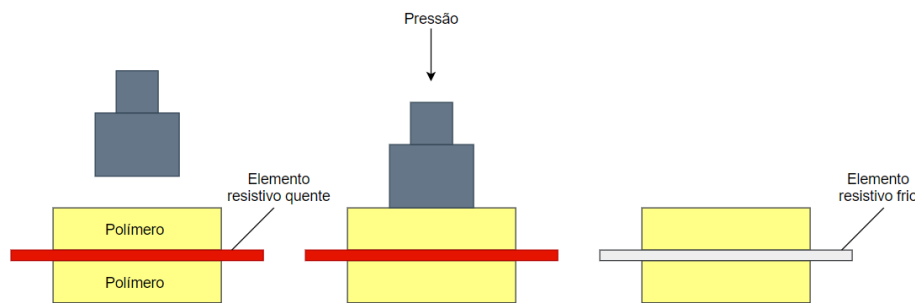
Soldadura por resistência. Adaptado de [44]
